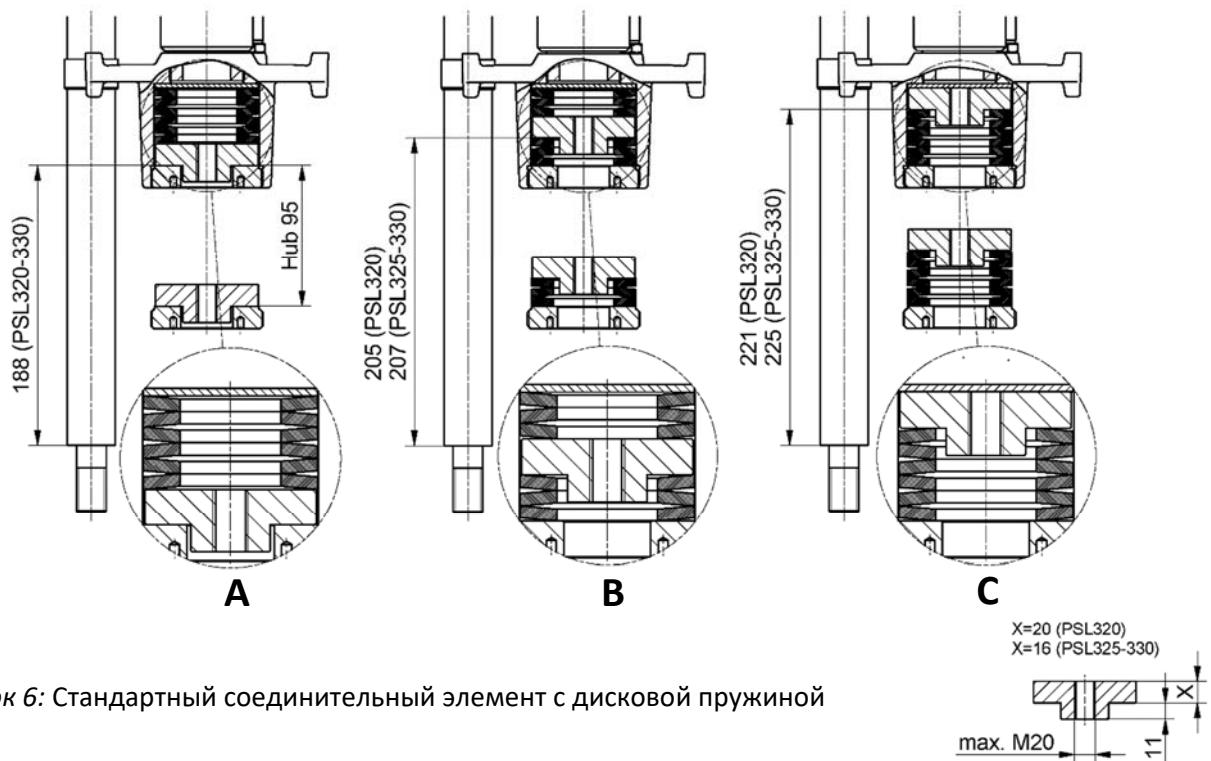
Стандартный соединительный элемент с дисковой пружиной
